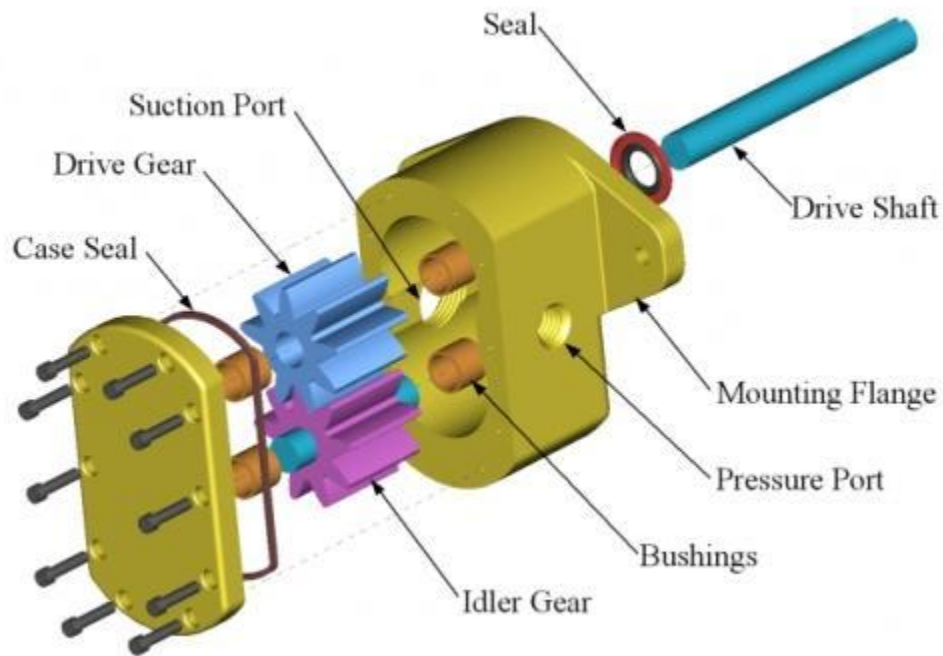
Dibujo de explosión de una bomba de engranajes [2]
